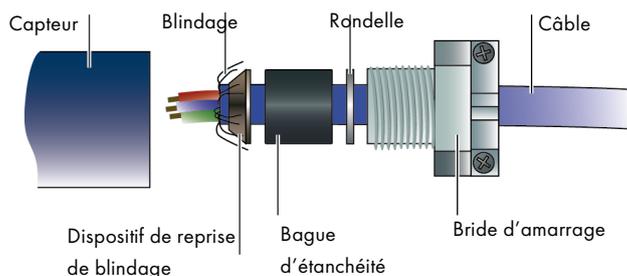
exemple de presse étoupe simple compression pour serrage sur câble souple
